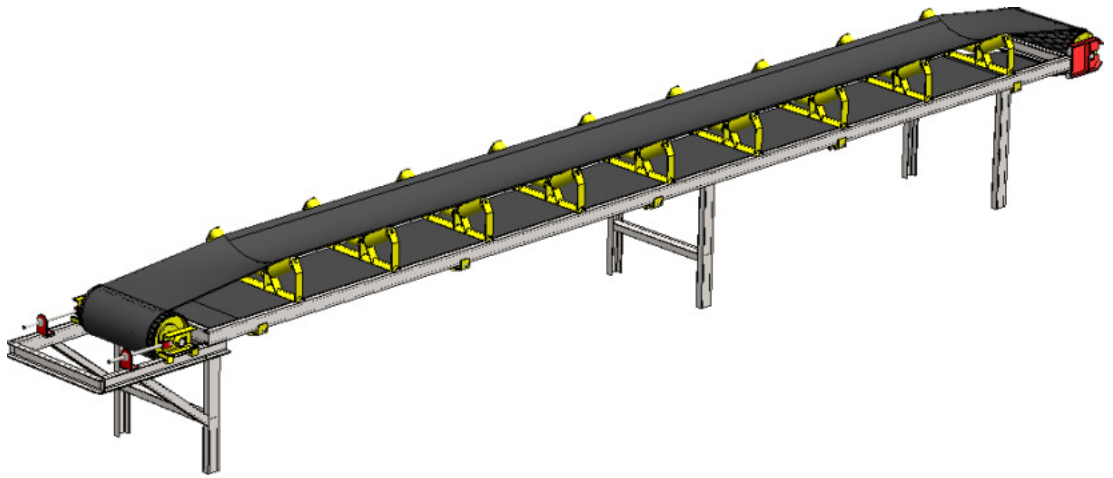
Bantlı konveyör montaj grupları şeması
